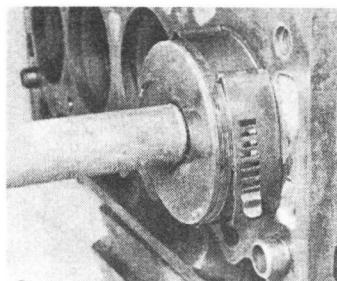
Установив на место компрессор для колец, приступите поршень в цилиндр
